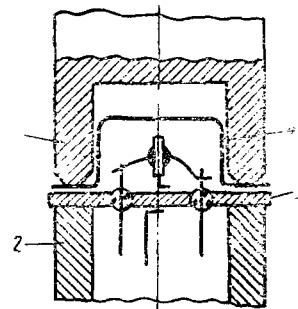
Схема контактной сварки корпуса транзистора с основанием:
